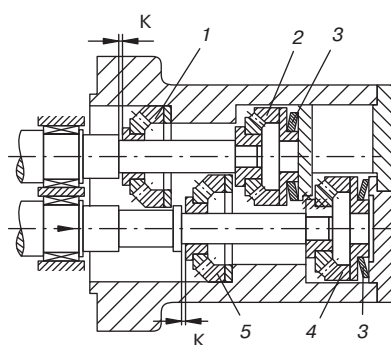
Схема узла подшипников двухшнекового экструдера с распределением усилий на упорные подшипники малого диаметра
